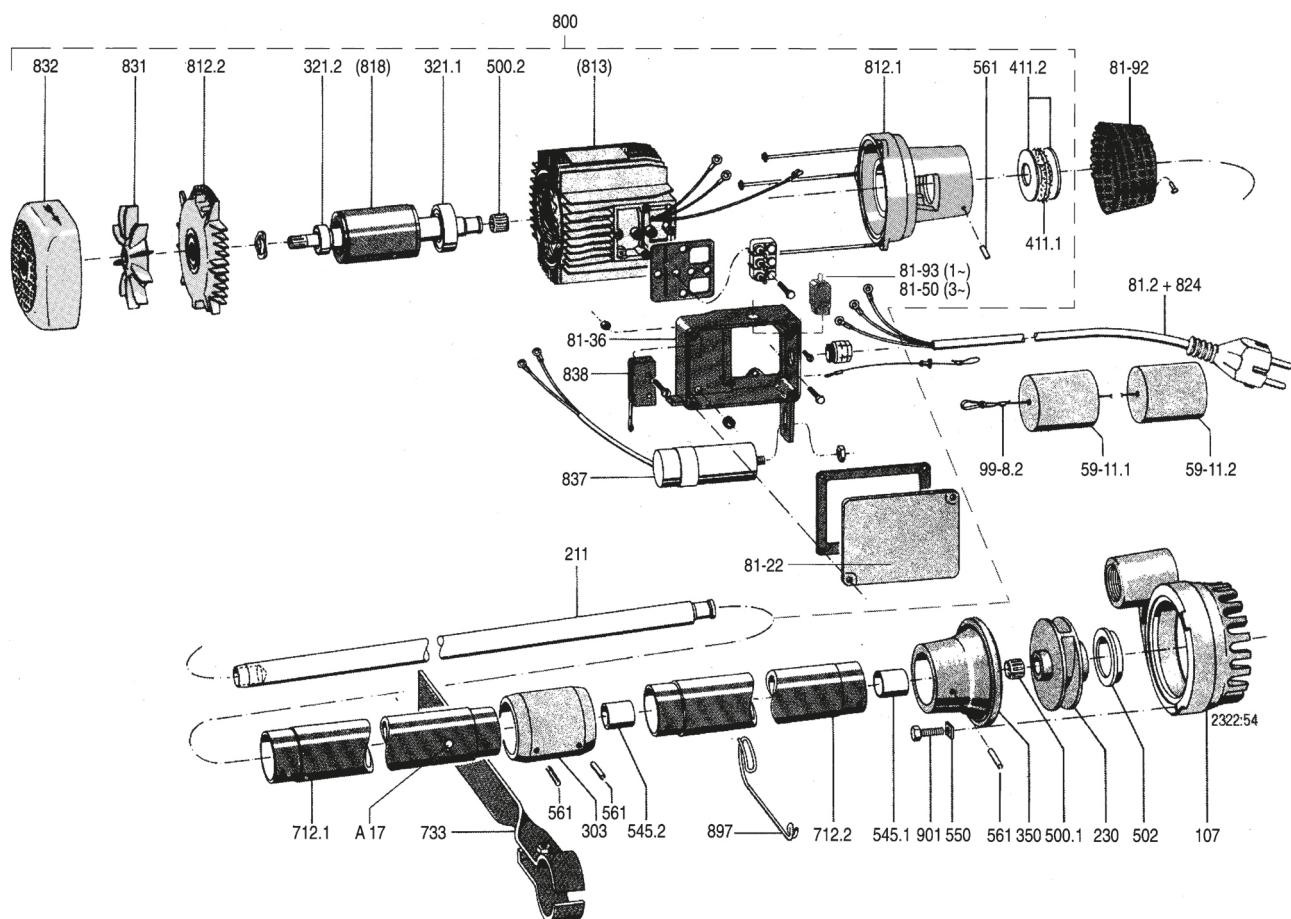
Explosionszeichnung - Rotex 10, 20 () = Als Ersatzteil nicht einzeln lieferbar
